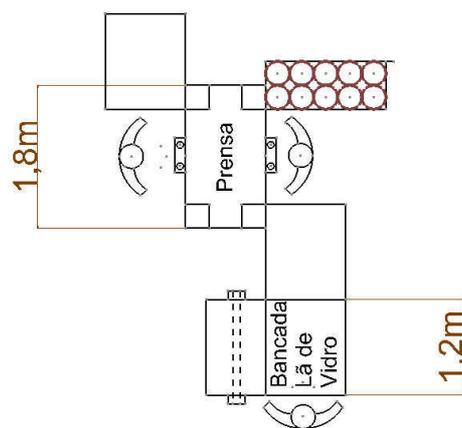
Detalhe Layout da área de preparação Lã de Vidro para prensagem.
